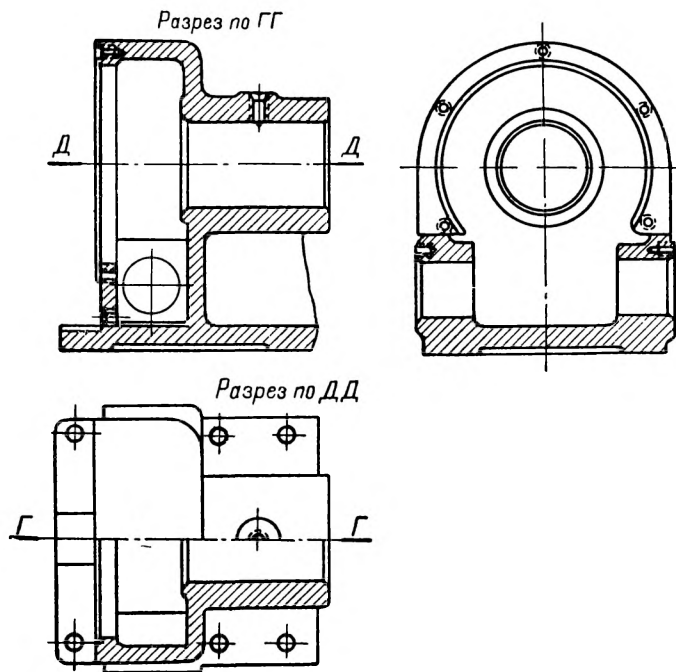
Вид продольного и поперечного разрезов детали на чертеже.
